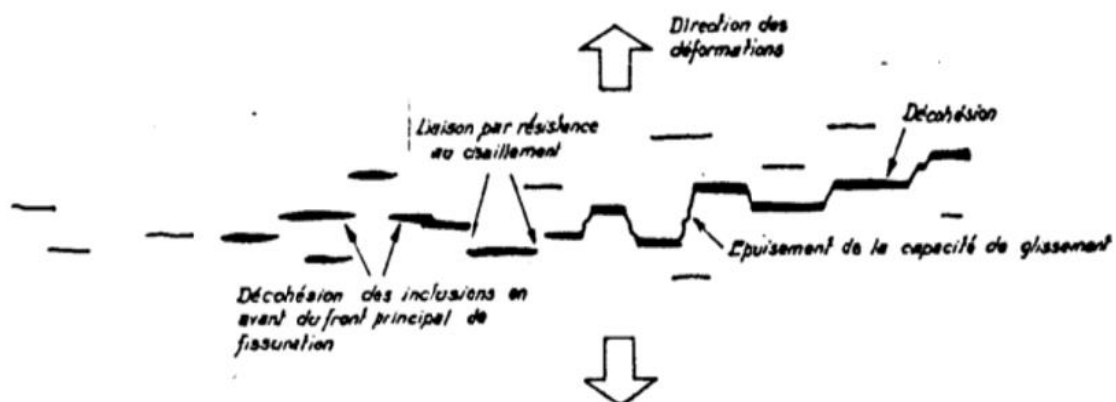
fissure par arrachement lamellaire dans le métal de base.
